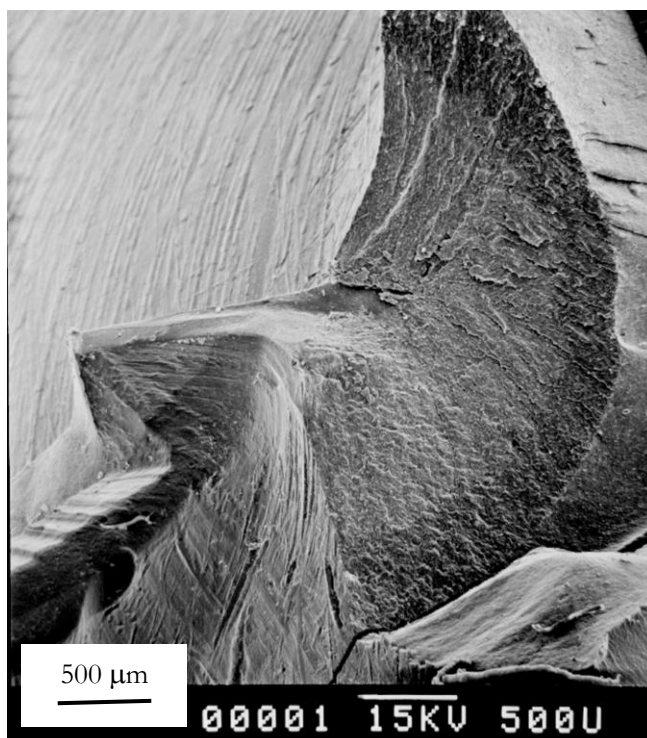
Essai AE42 – Zone d'amorçage sur joint
